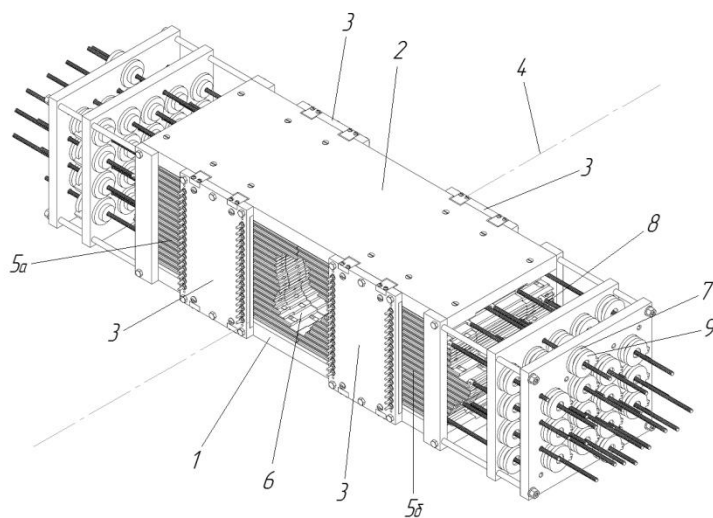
Конструкция многолепесткового коллиматора на 33 пары пластин с индивидуальными приводами и датчиками положения
